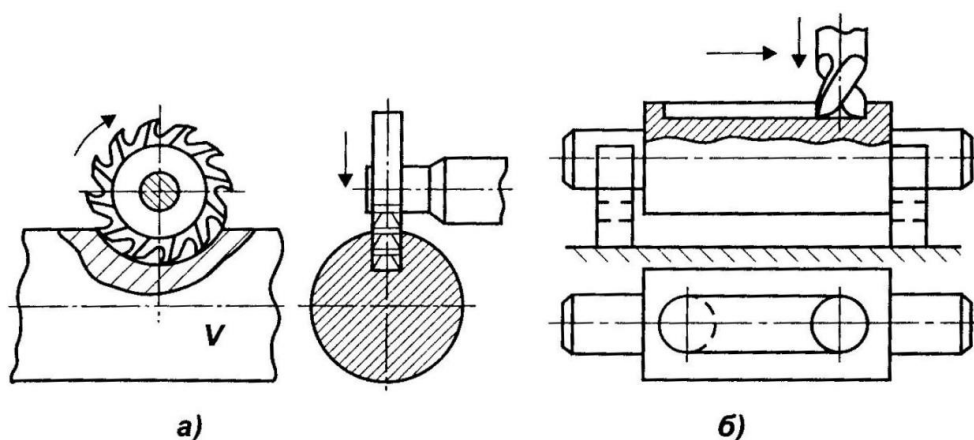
Схеми фрезерування шпонкових пазів на валах
